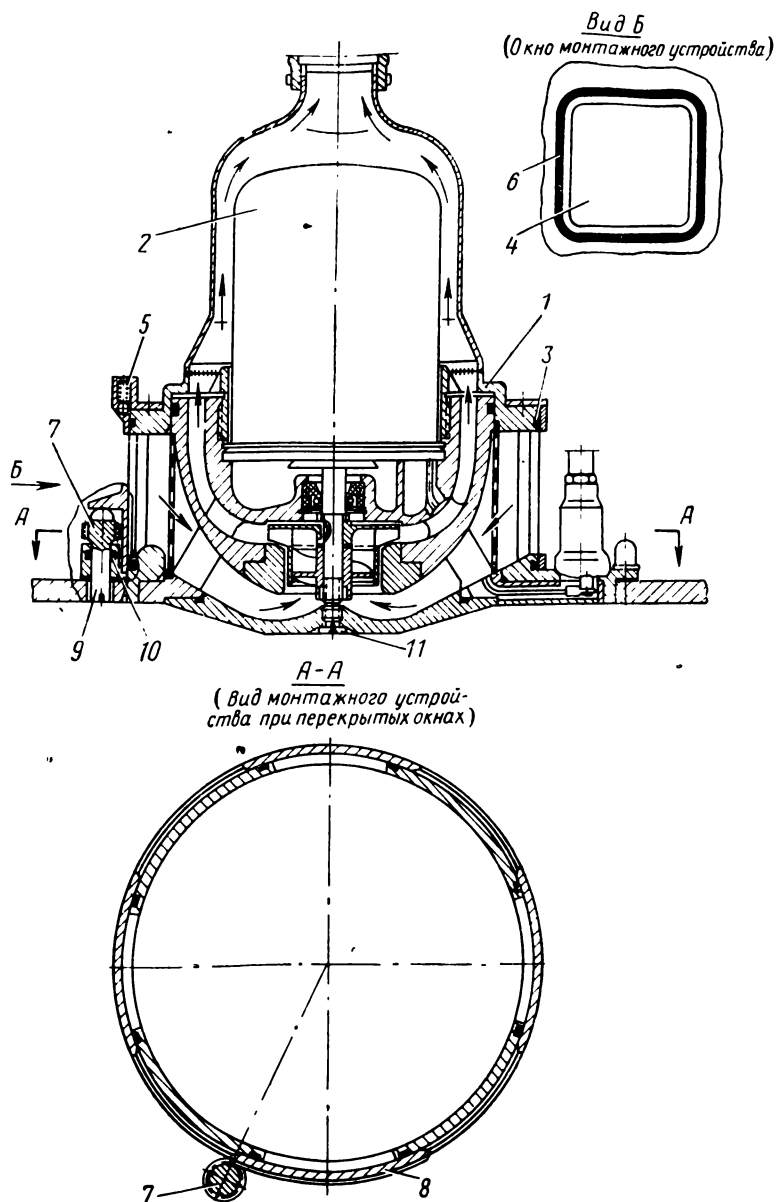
Кессонное монтажное устройство для монтажа и демонтажа насосного агрегата без слива топлива из кессона:
